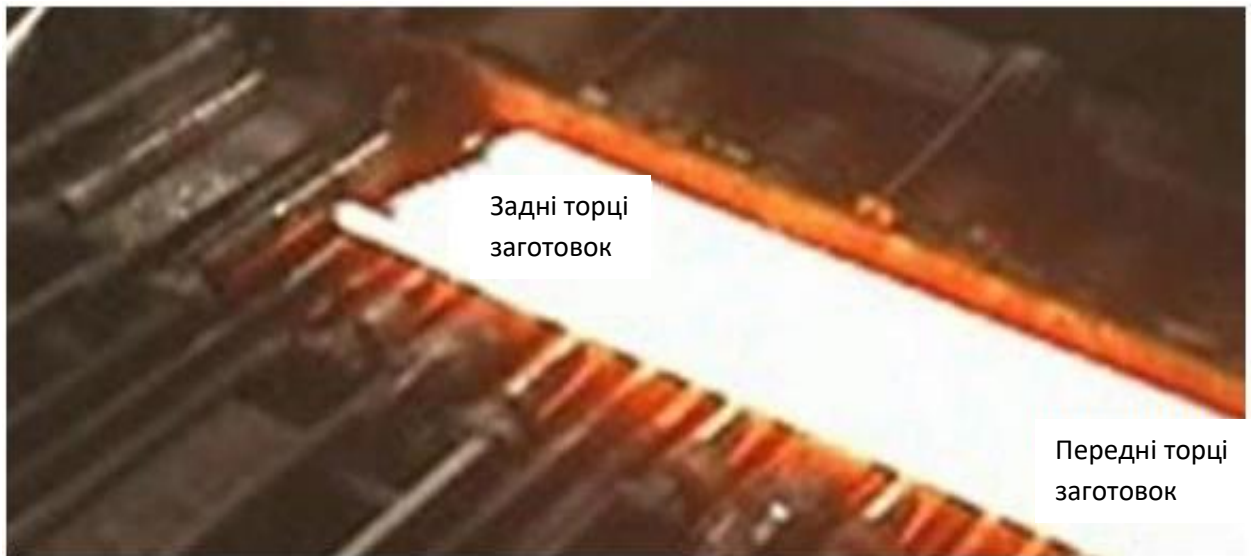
Пакет заготовок після розкрою однієї штанги (передні торці вирівняні)
